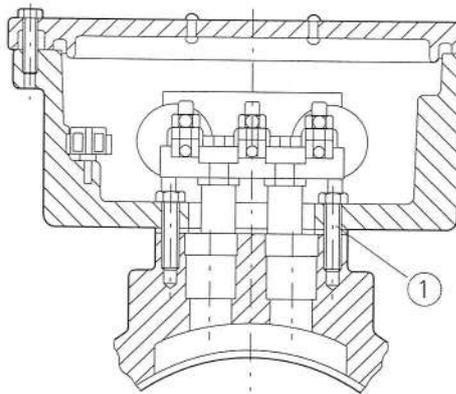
Klemmenkasten mit Befestigungsschraube ①
